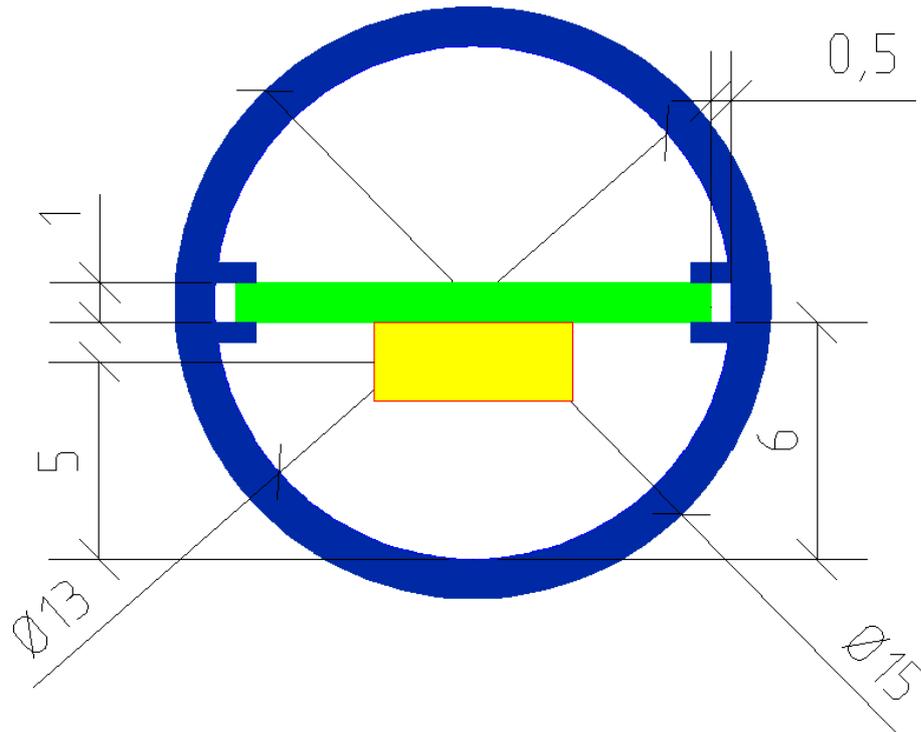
Размеры корпуса светильника для локального освещения, его длина 400 мм
